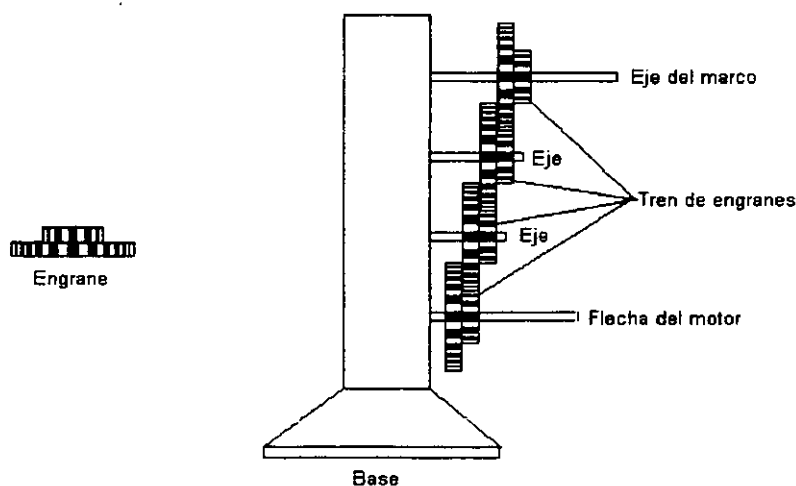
Engrane y conjunto de engranes formando el tren de engranes
